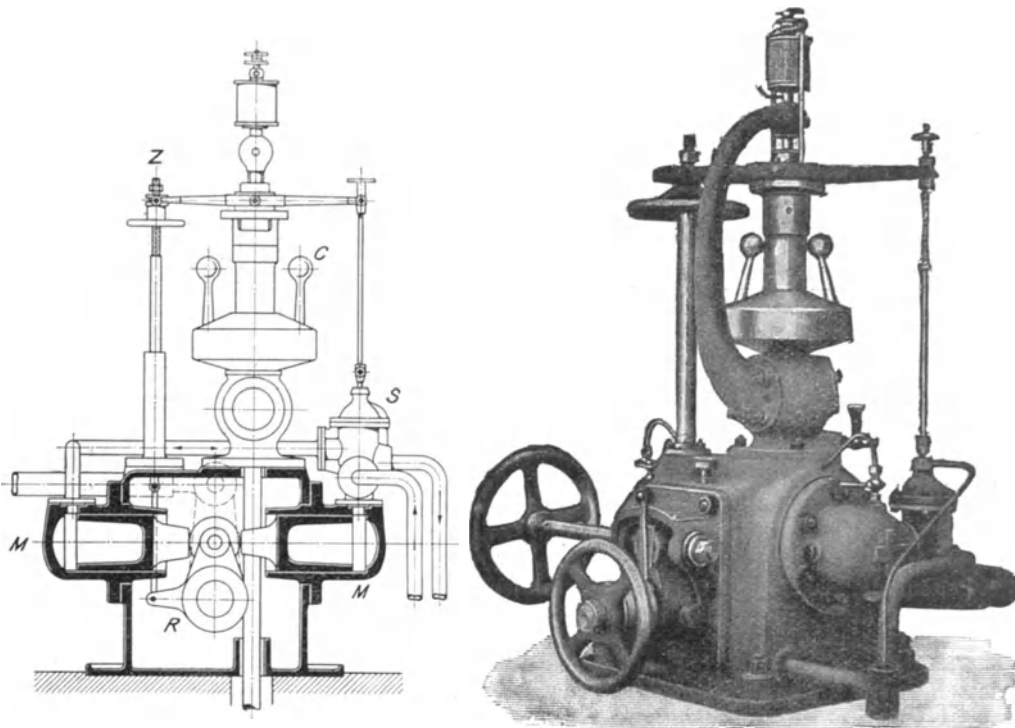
bis 146. Universal-Regulator von Escher Wyfs & Co.
